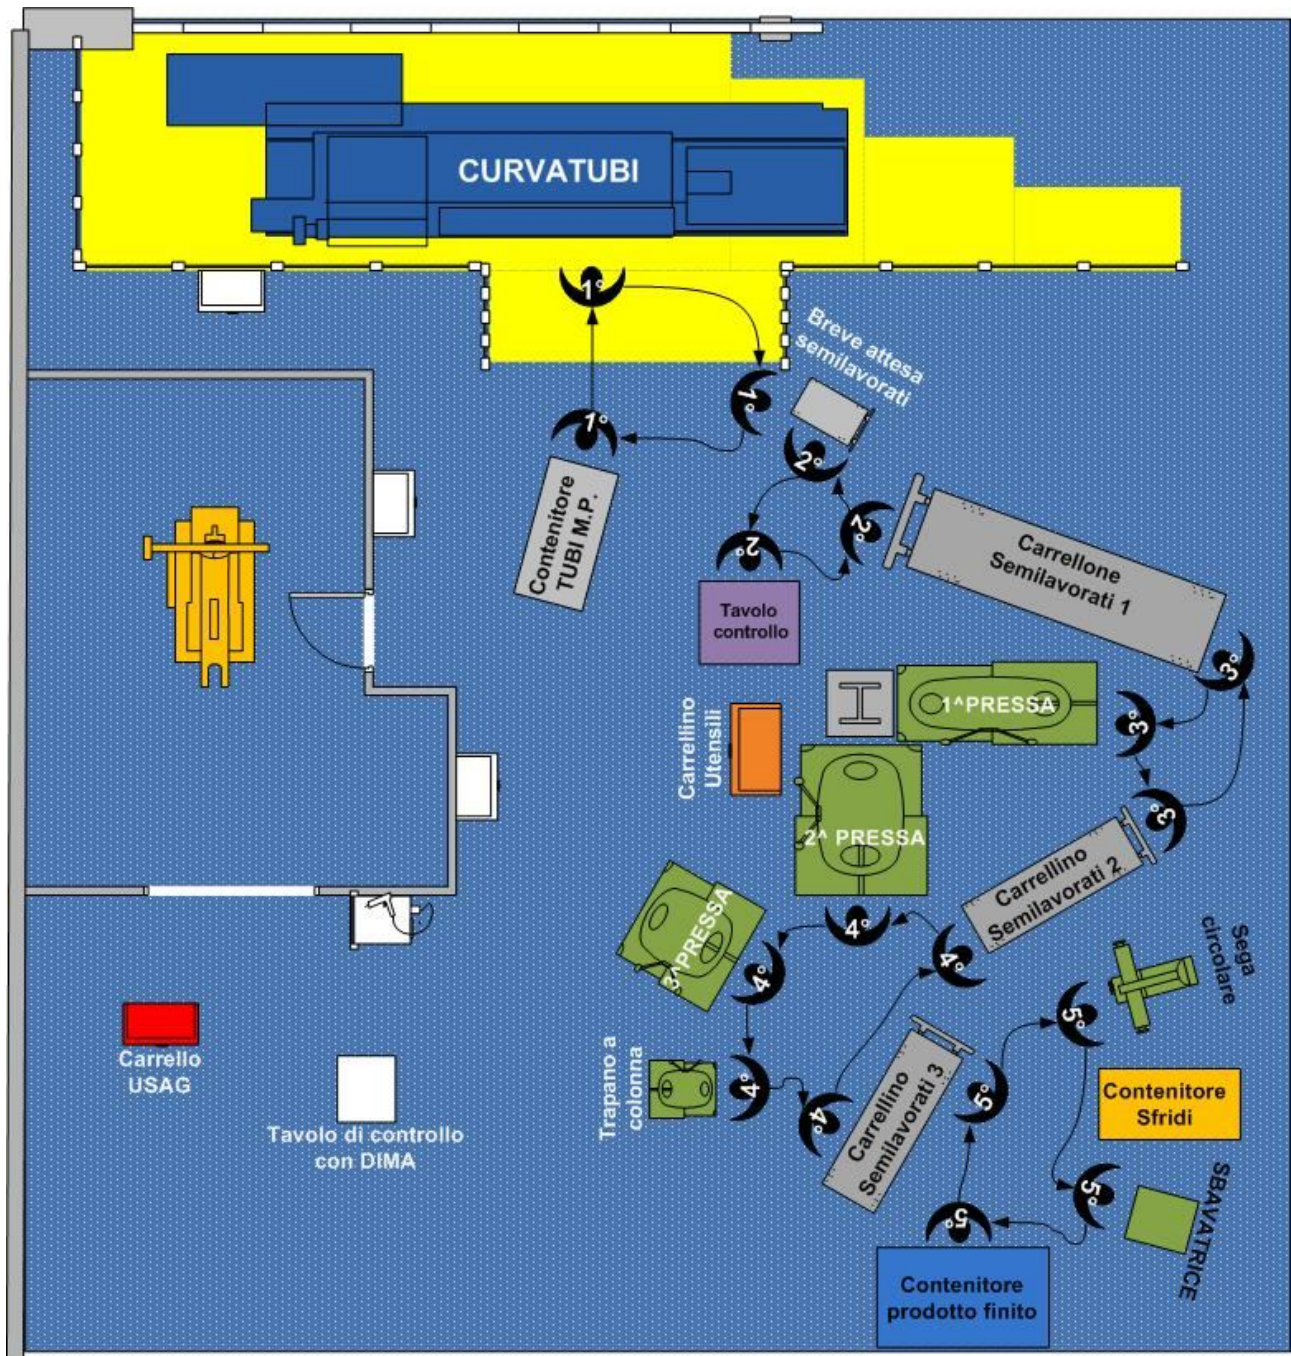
Lay-out dell'isola di lavoro più ampia dello stabilimento con anche i movimenti degli operai
